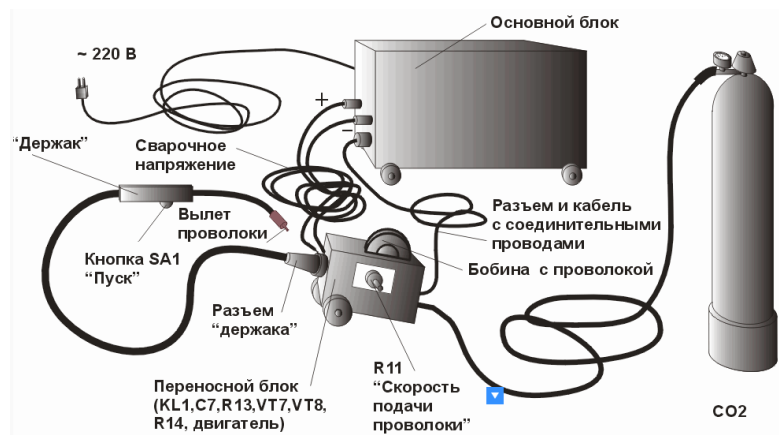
Сварочный полуавтомат в углекислой газовой среде
